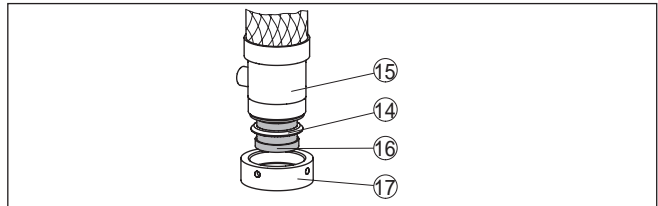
Montagem da refrigeração do cindilador - parte inferior
